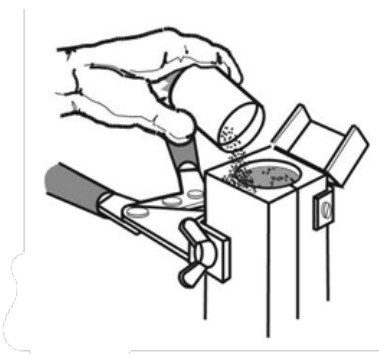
Espolvorear el polvo de ignición sobre la soldadura y depositar aprox. un 25 % sobre el borde del molde
